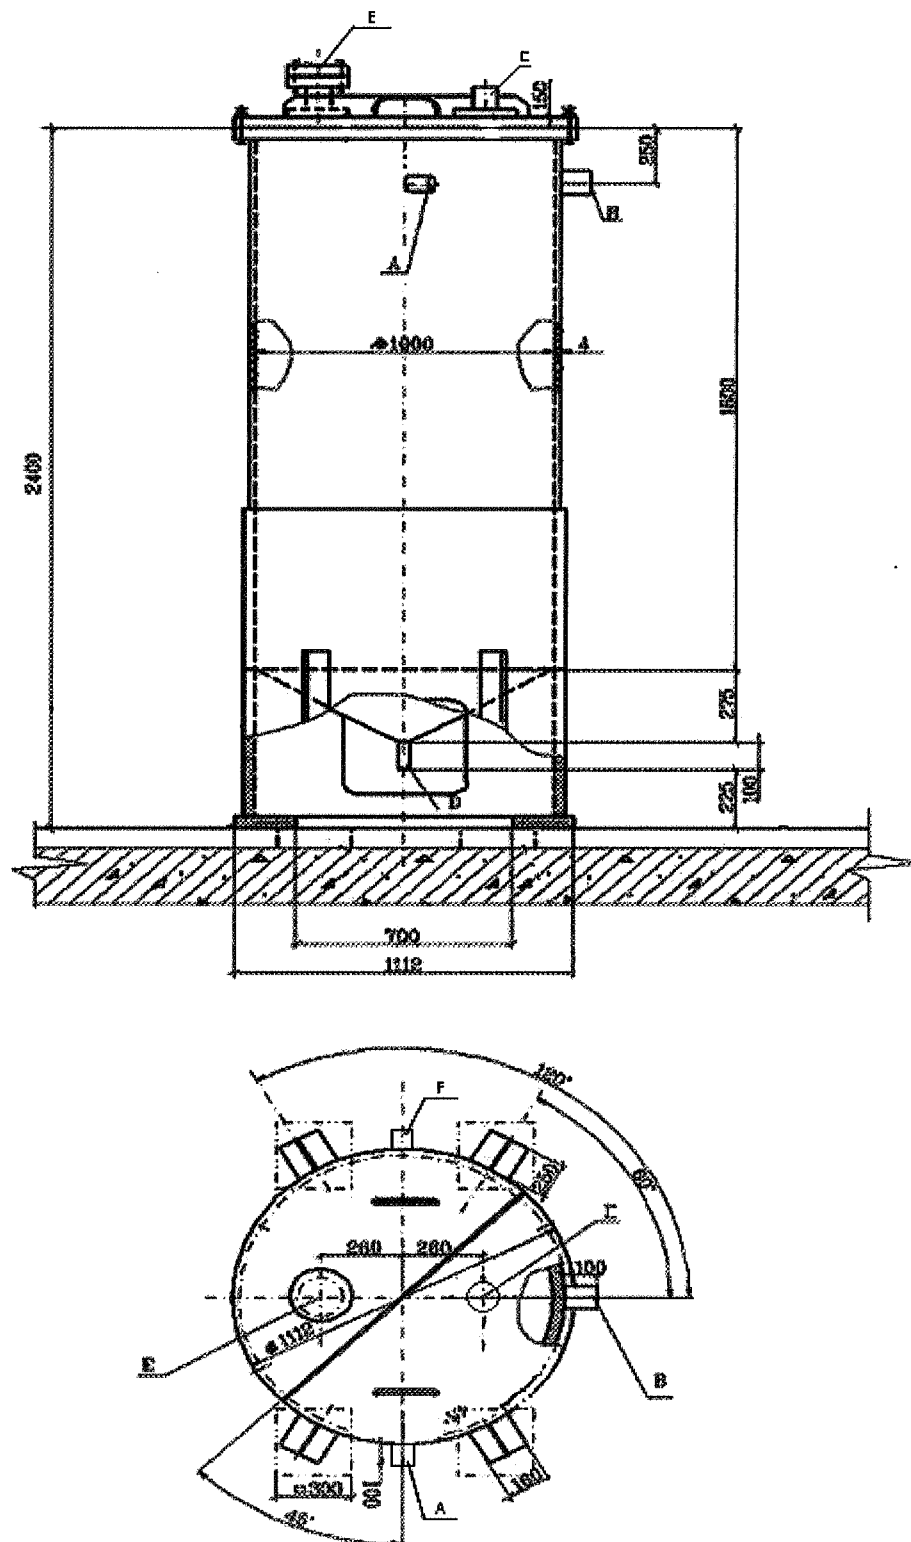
Габаритный чертеж мерника гидразина LDN10BB001, LDN10BB002
